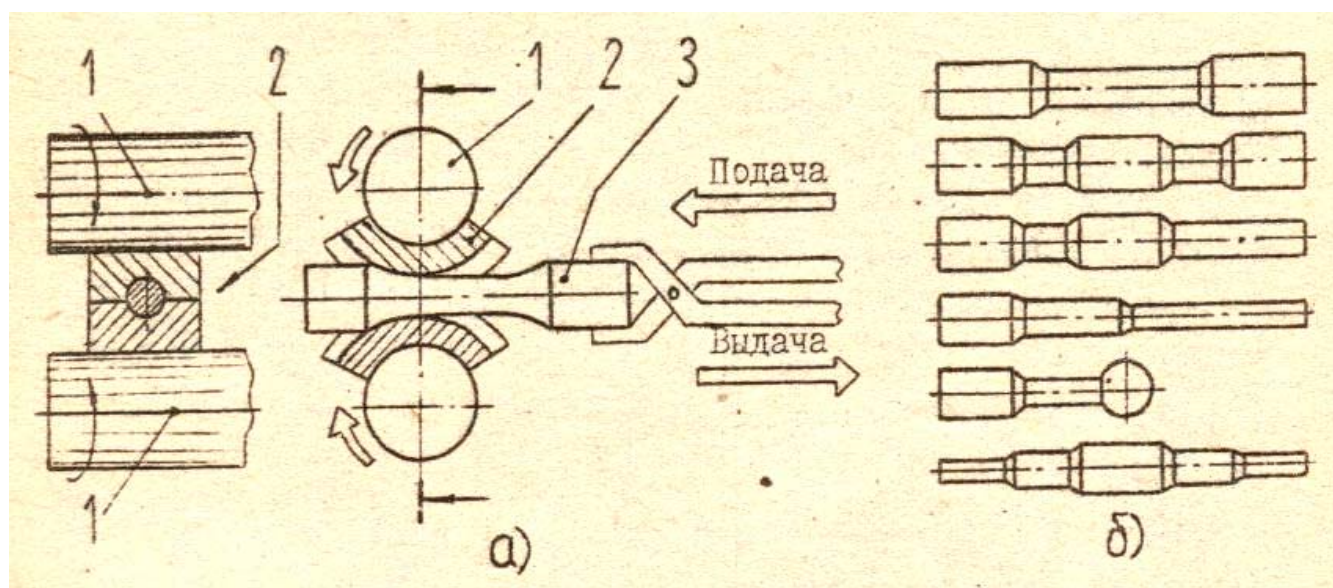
Схема вальцовки на консольных ковочных вальцах (а) и типовые поковки (б): 1 — валки; 2 — штампы-секторы; 3 — обрабатываемая заготовка
